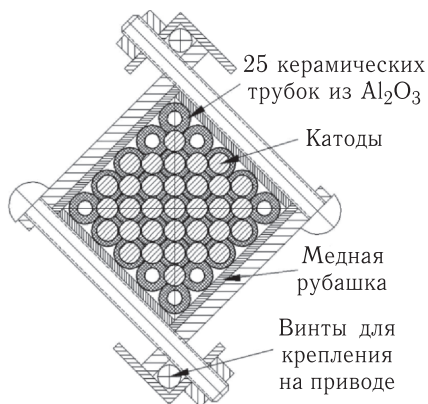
Схема размещения катодов в сборке из трубок, изготовленных из оксида алюминия  $Al_2O_3$
